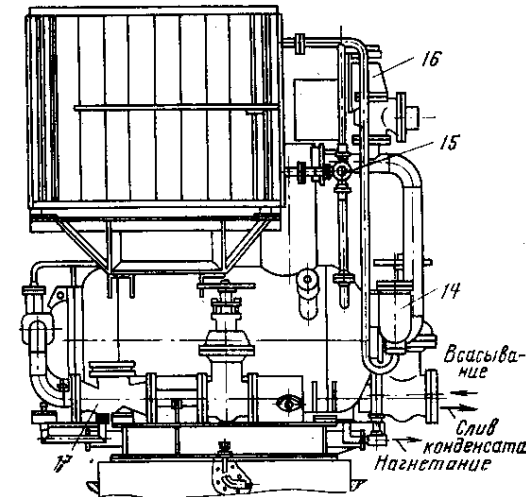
Компрессорная установка 5ВГК-10/6:
